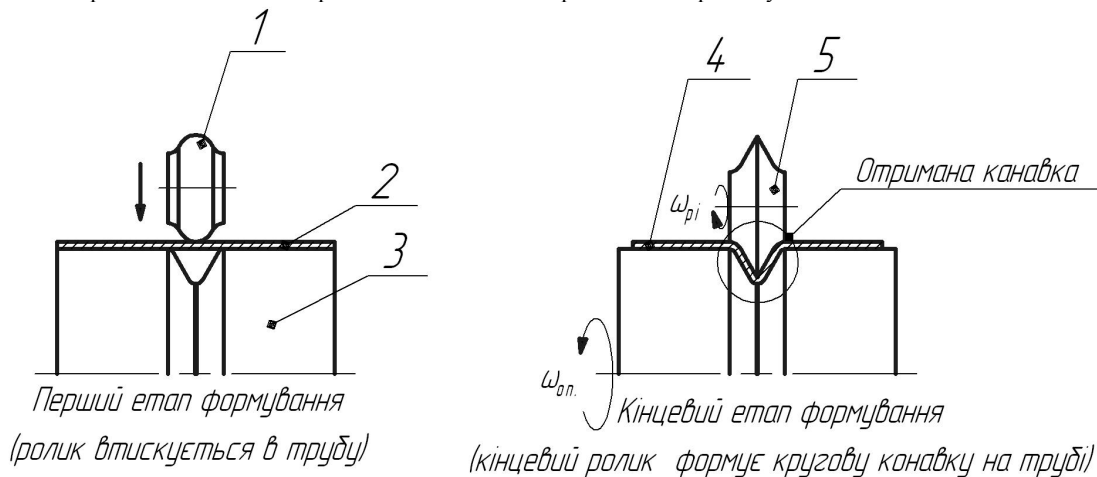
Схема процесу обкочування: 1 – перший ролик, 2 – заготовка, 3 – оправка, 4 – отримана деталь, 5 – кінцевий восьмий ролик
